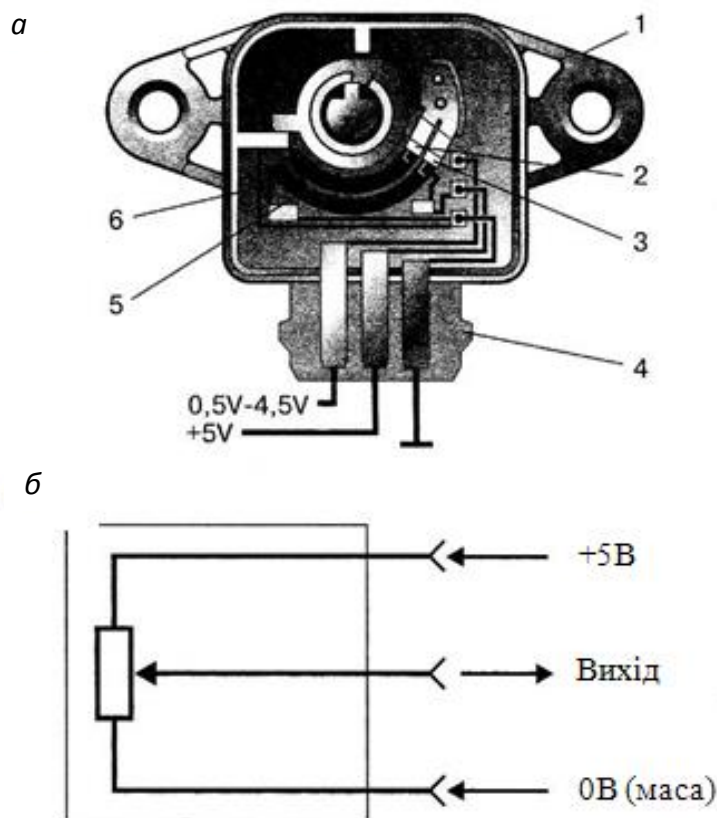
Датчик положення дросельної заслінки потенціометричного типу: конструкція (а); схема підключення (б); 1 – корпус; 2,3 – ковзні контакти; 4 – рознімання; 5,6 – резистивні доріжки
